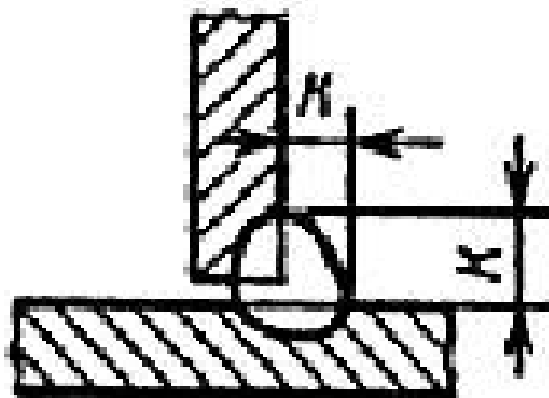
Конструктивные элементы сварочного шва, согласно ГОСТ 14771-76.
